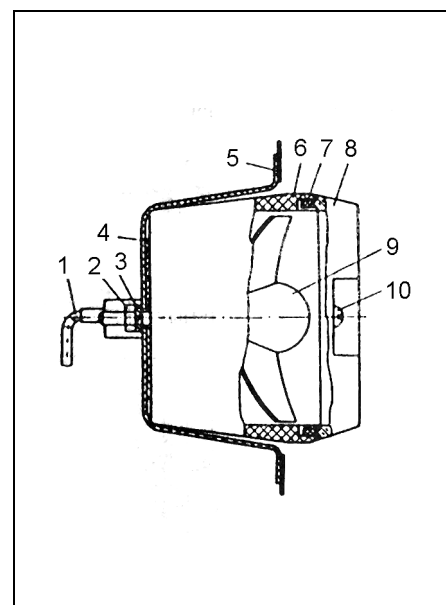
Фонарь заднего хода: 1 – провод основного пучка проводов; 2 – гайка крепления фонаря; 3 – шайба пружинная; 4 – прокладка; 5 – кузов; 6 – корпус фонаря заднего хода в сборе; 7 – прокладка рассеивателя; 8 – рассеиватель; 9 – лампа; 10 – винт.
